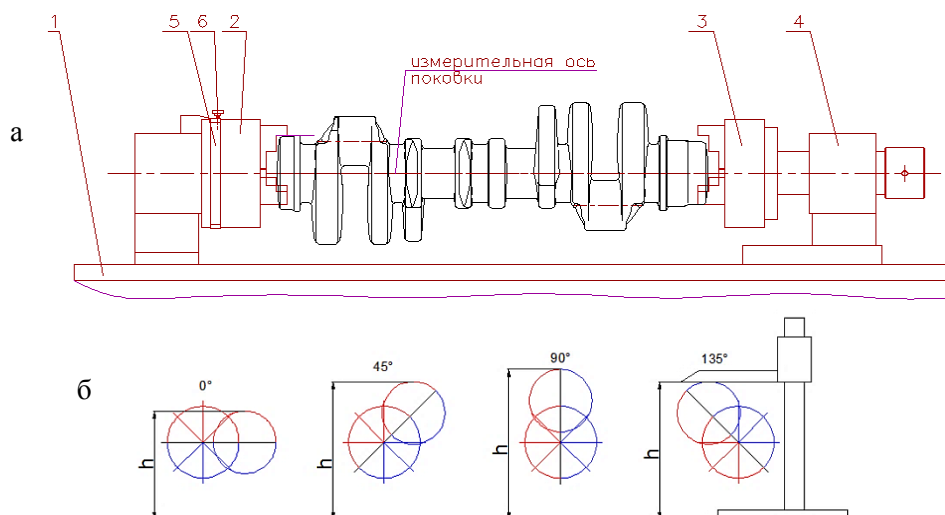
Контрольное приспособление координатных измерений высотных параметров: а – конструкция приспособления: 1 – станина; 2, 3 – патрон самоцентрирующий; 4 – корпус; 5 – угловой вращающийся лимб; 6 – стопорный винт лимба; б – пример последовательности измерений высотных параметров в различных угловых фазах
